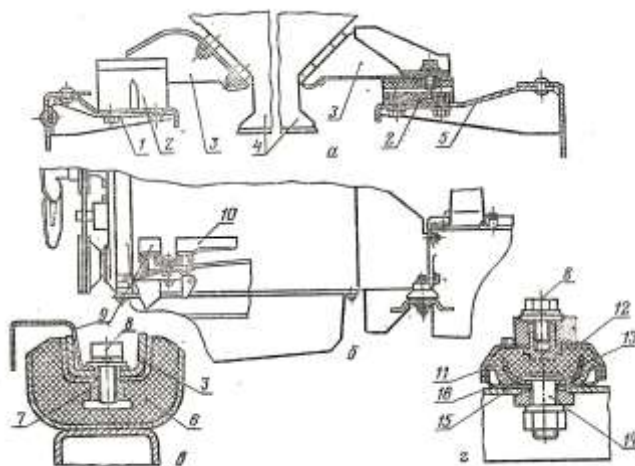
Крепление двигателя ГАЗ-53 к раме:
